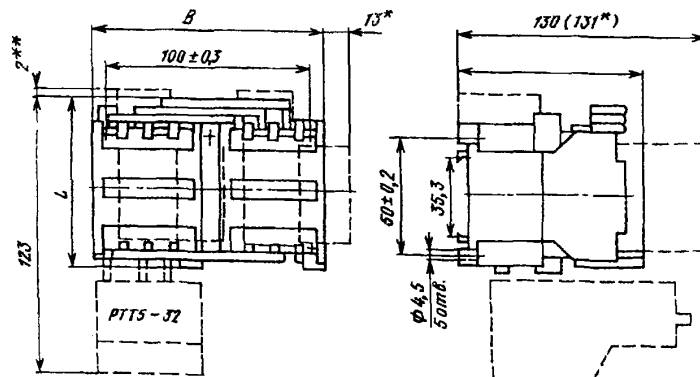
Габаритные и установочные размеры реверсивных пускателей (ПМ12-032)
